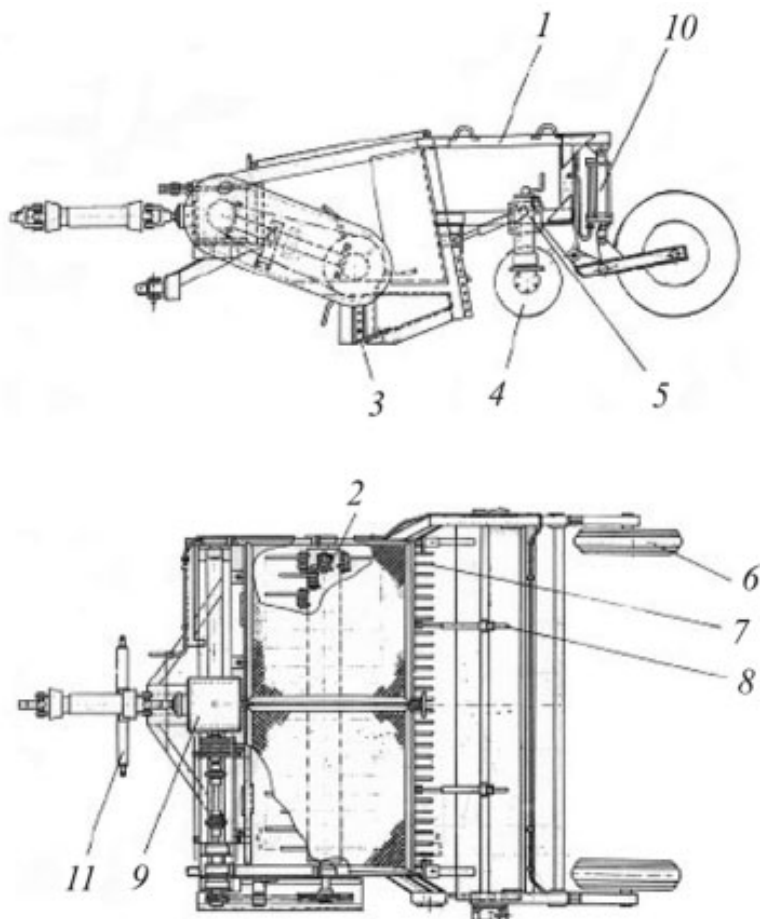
Машина роторная почвообрабатывающая МРП – 2,1: 1 – рама; 2 – ротор; 3 – лемех; 4 – каток; 5 - подвеска катка; 6 - колеса ходовые; 7 – дека; 8 - амортизаторы; 9 - механизм привода; 10 – гидросистема; 11 - прицепное устройство.
